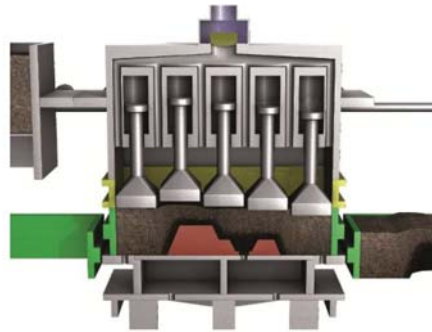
Облицованные тефлоном рабочие плунжеры и корпус цилиндров многоплунжерной головки гидравлического прессования
